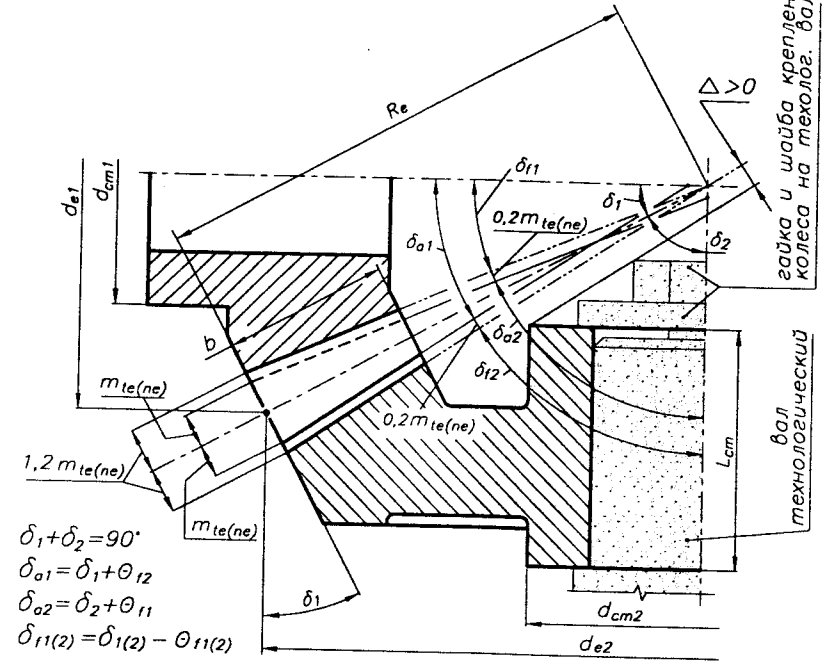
Зубчатые колеса с осевой формой зуба I и постоянным радиальным зазором по ширине зубчатого колеса
